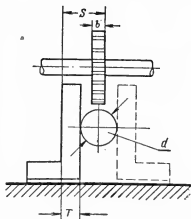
Схема установки дисковой фрезы при фрезеровании канавки для призматической шпонки:
